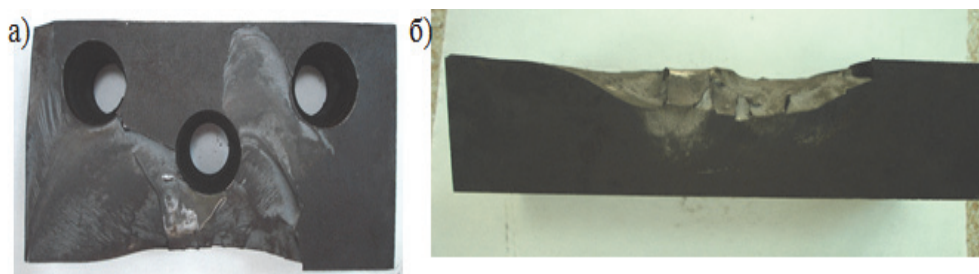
Внешний вид ножа: а - зона радиального строения; б - очаг разрушения
